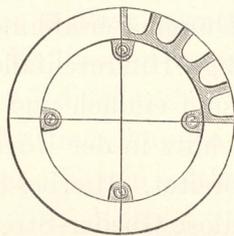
Horizontale Säscheibe der Kartoffellegemaschine von Gebr. Adam, Greifenhagen.
